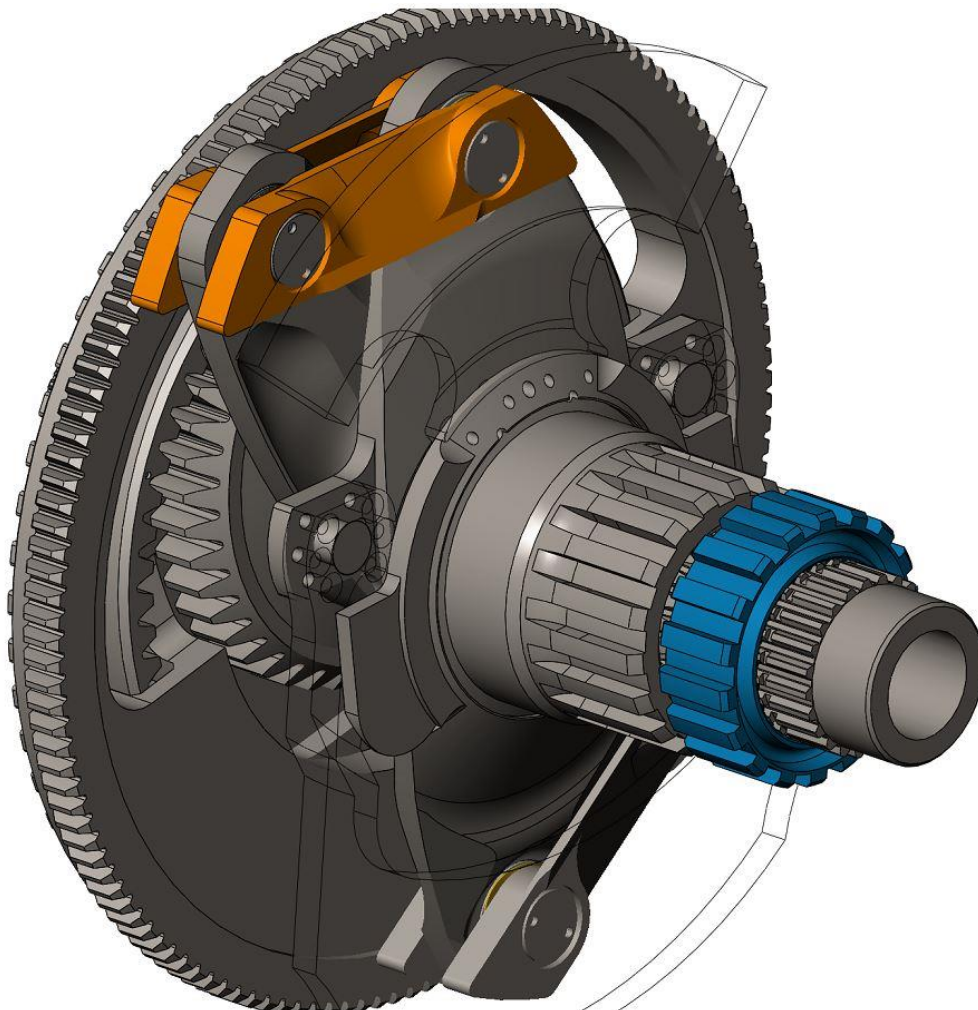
Загальний вигляд силового механізму (варіант 3)
